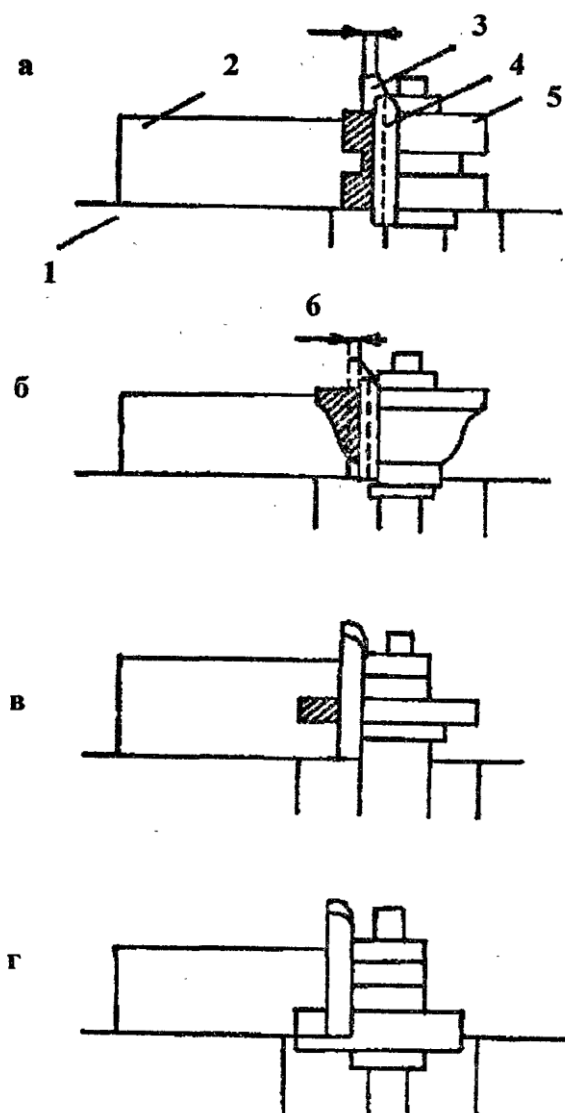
Схема обробки на фрезерному верстаті: а – гребня; б – плінтуса; в – шпунта; г – фальца; 1 – стіл; 2 – деталь; 3,4 – лінійки; 5 – фреза; 6 – припуск.
